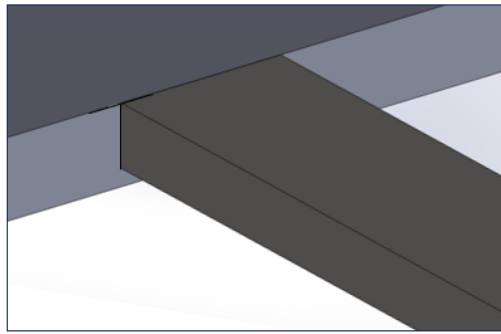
Hipótese 2 para a ligação entre as barras do suporte (apenas soldadura).
